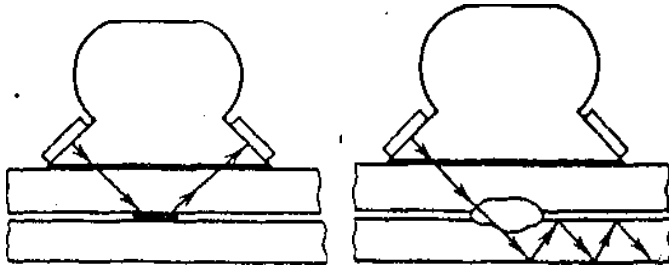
Схема прохождения ультразвука в сварной точке.
